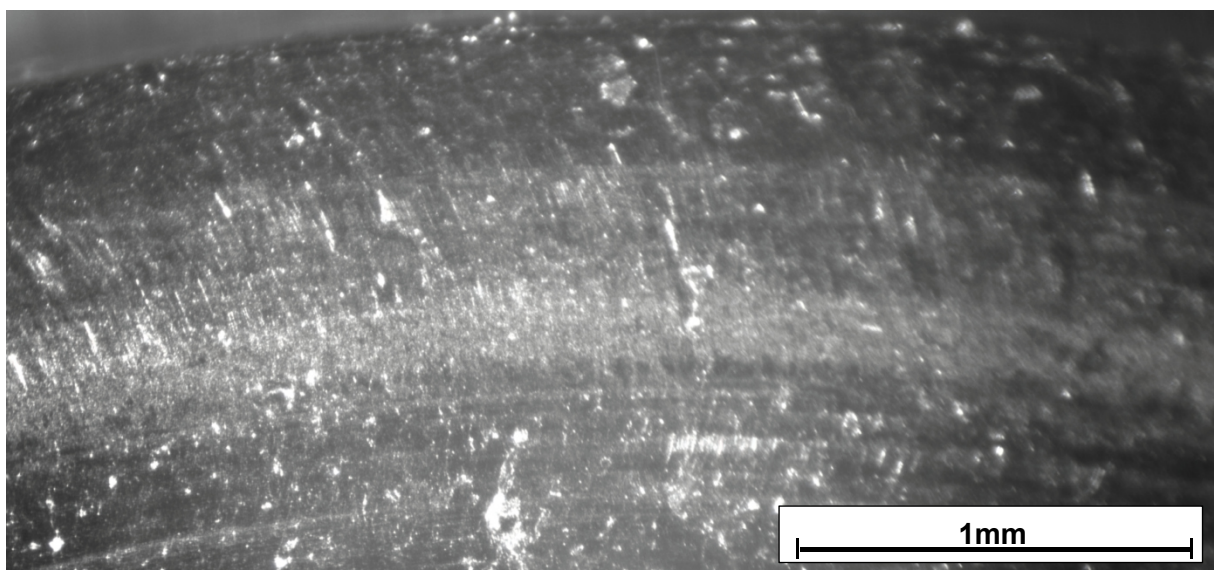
Gleitfläche der Trapezgewindespindel des Zustands „+SH“
